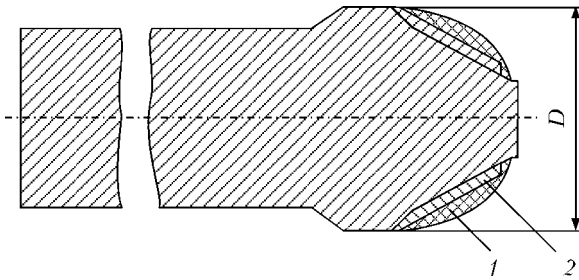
Схемы разделки и наплавки штоков DN 50: 1 — наплавленный металл до механической обработки; 2 — то же после механической обработки
